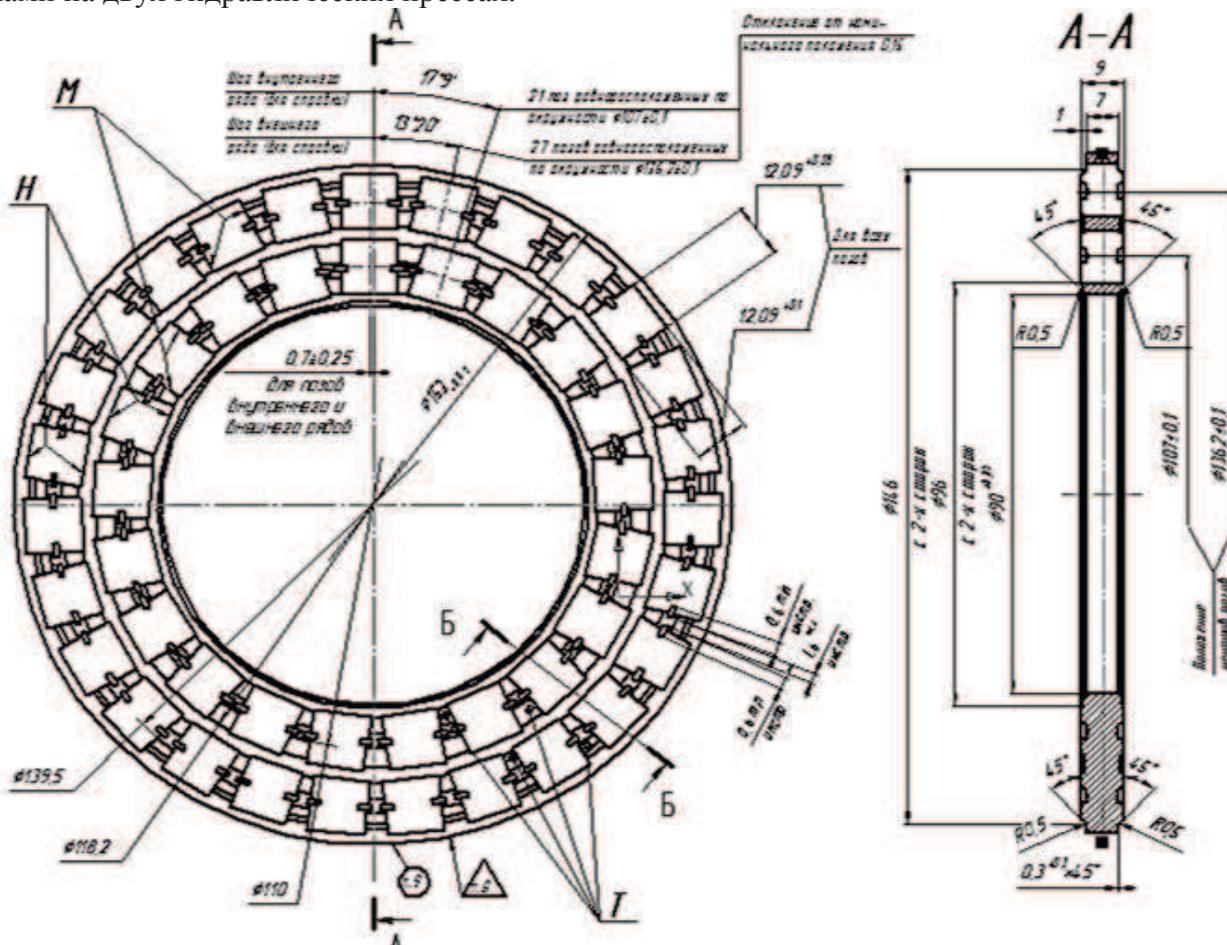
Сепаратор упорного подшипника с квадратными гнёздами
